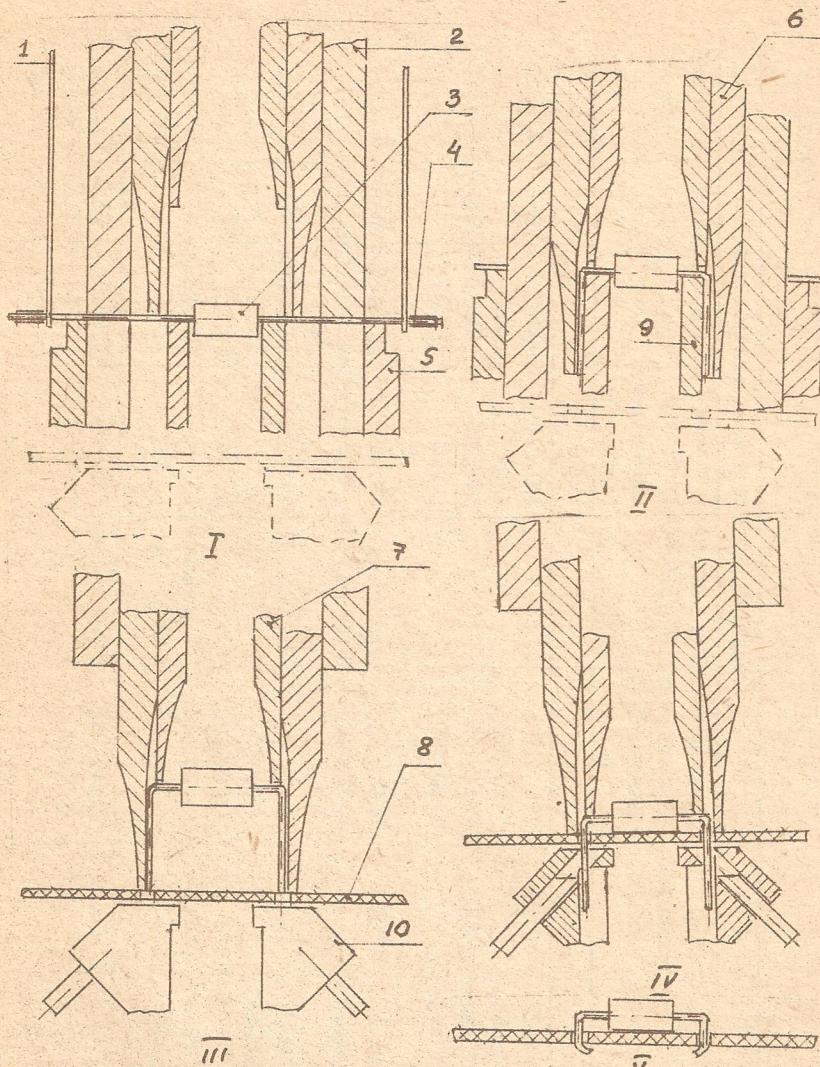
Рис. I. Схема работы укладочной головки: 1 - колесо периодической подачи ленты с ЭРЭ; 2 - пuhanсон обрезки выводов ЭРЭ; 3 - ЭРЭ, вклеенное в ленту; 4 - лента; 5 - матрица обрезки; 6 - пuhanсонгибки; 7 - толкатель устройства досылки ЭРЭ; 8 - плата; 9 - матрица гибки; 10 - нижняя подгибочная головка. Последовательность работы головки: I - вырезка ЭРЭ; II - гибка выводов ЭРЭ; III - застакивание выводов ЭРЭ в монтажные отверстия платы; IV - подрезка и подгибка выводов ЭРЭ снизу; V - ЭРЭ установлен
